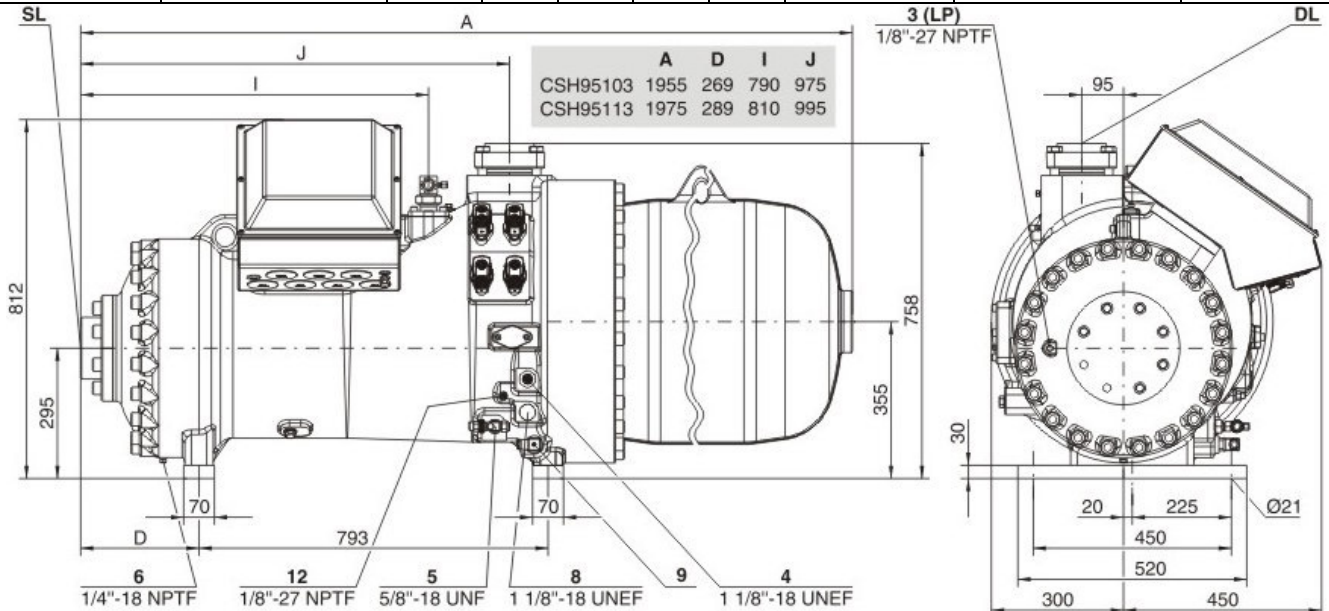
Загальний вигляд компресора Bitzer CSH95113-320Y
